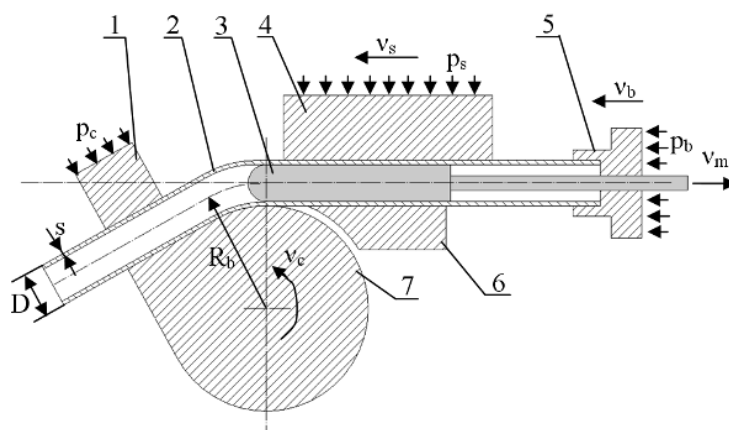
Схема гибки намоткой: 1 – передний прижим; 2 – заготовка; 3 – дорн; 4 – задний прижим; 5 – бустер; 6 – складковыглаживатель; 7 – гибочный ролик
